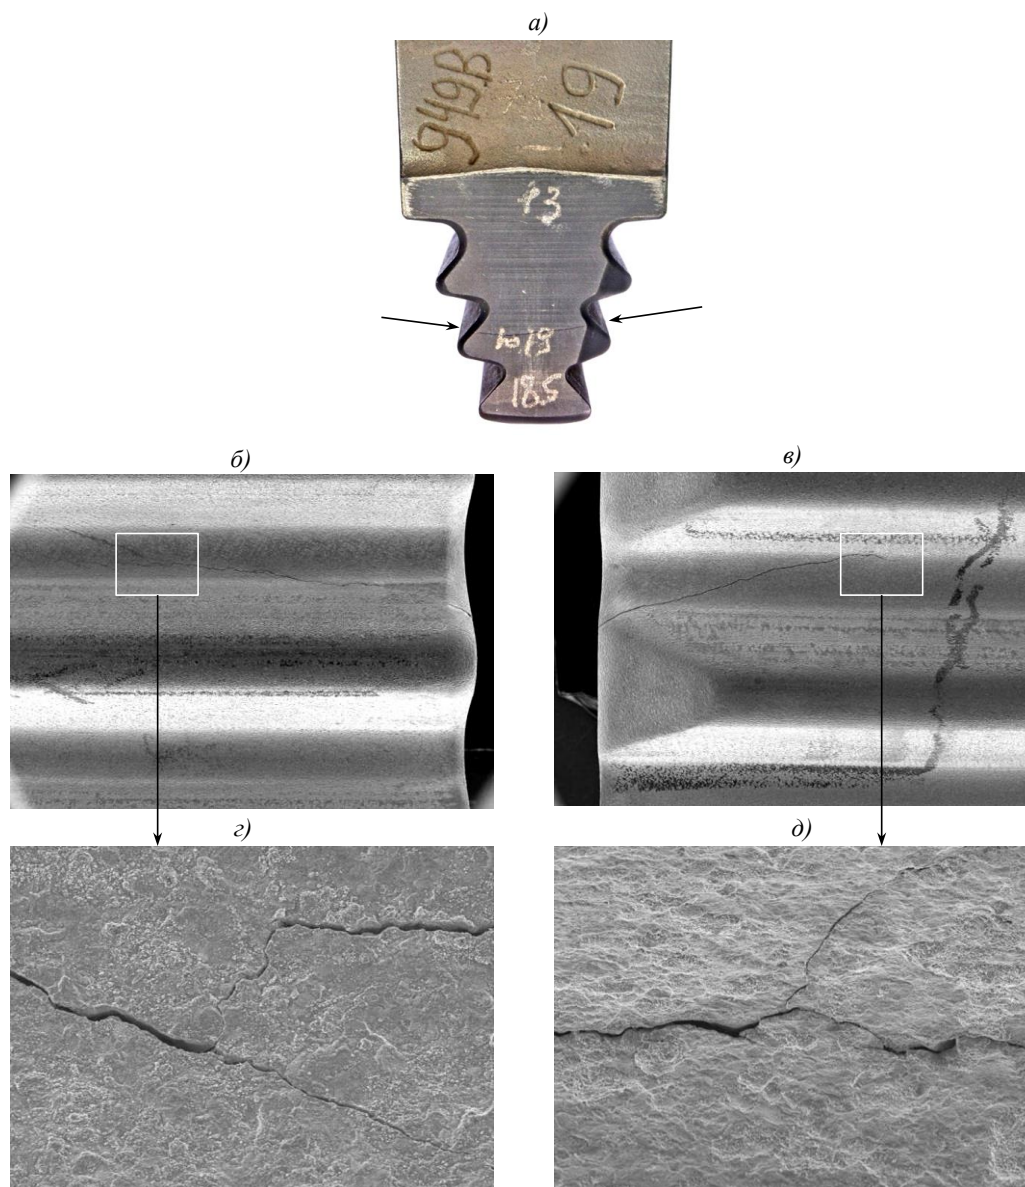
Разрушение рабочей лопатки 1 из сплава ЖС32-ВИ:
